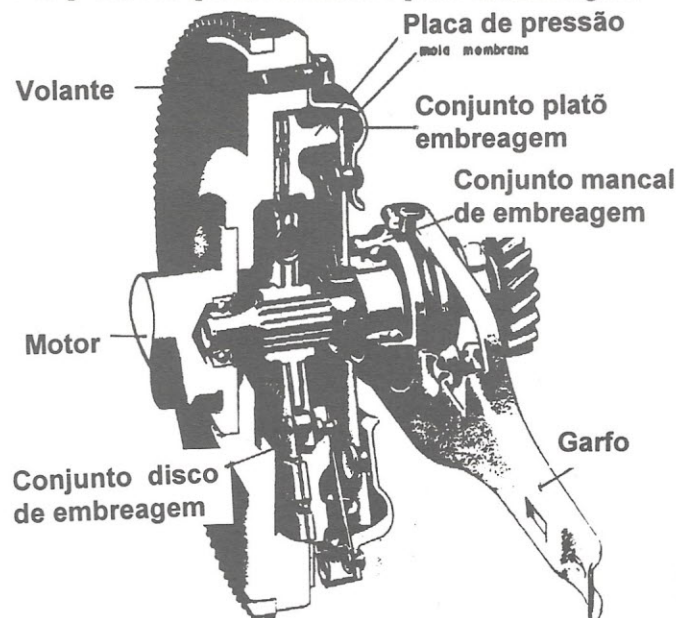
Conj Platô de Embreagem montado no volante do motor.
